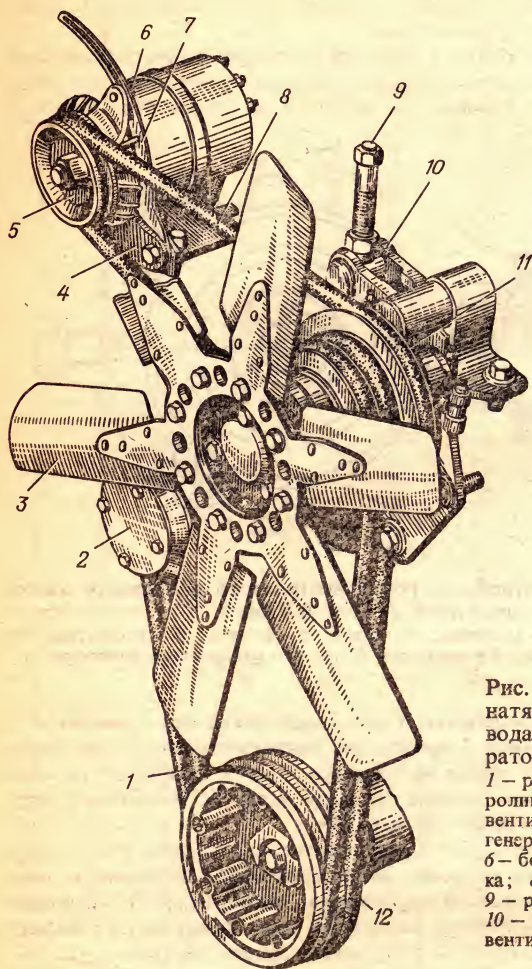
Устройство для натяжения ремней привода вентилятора и генератора двигателя Д-130Т: 1 — ремень вентилятора; 2 — ролик натяжения ремня; 3 — вентилятор; 4 — кронштейн генератора; 5 — генератор; 6 — болт крепления; 7 — планка; 8 — ремень генератора; 9 — регулировочный винт; 10 — кронштейн; 11 — шкив вентилятора; 12 — шкив коленчатого вала
